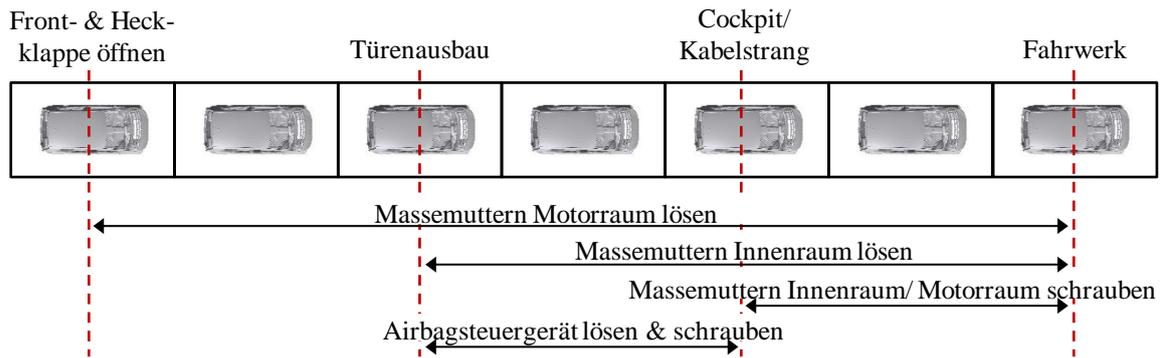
Fügeabfolge Massemuttern & Airbagsteuergerät
